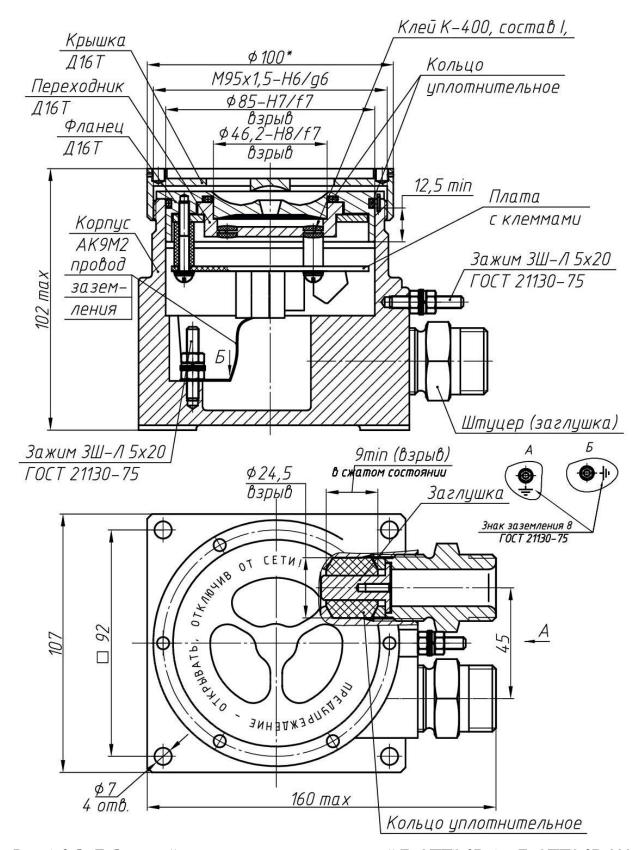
б - Габаритный чертёж звуковых оповещателей ExOПП3-2B-A и ExOПП3-2B-220-A в алюминиевом корпусе (вариант), совмещённый с чертежом взрывозащиты. Маркировка показана в п. 1.6.
